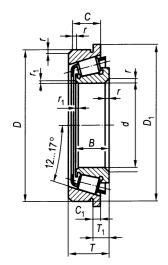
Подшипник роликовый радиально-упорный конический однорядный с бортом на наружном кольце
